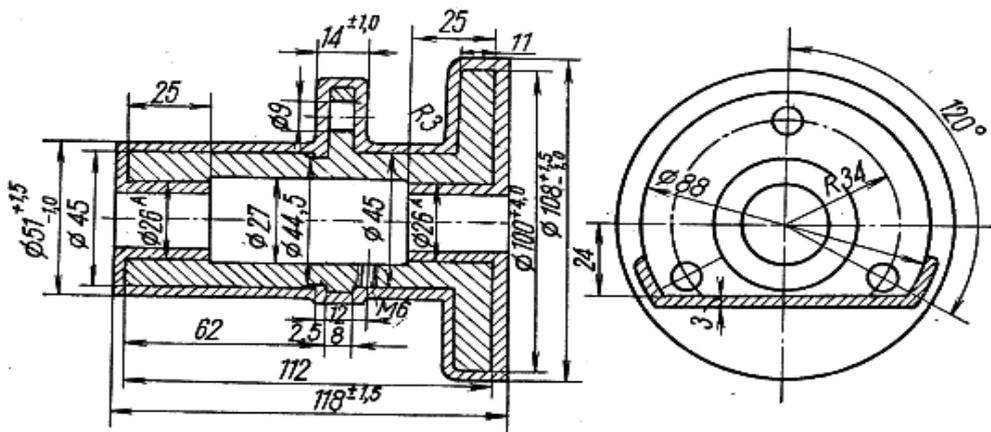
Заготовка чавунної втулки у вигляді виливка
